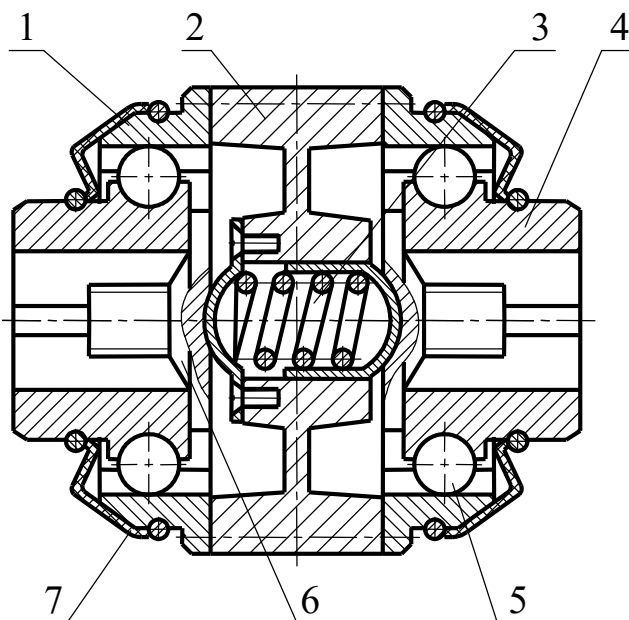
Кулькова компенсуюча муфта: 1 - обойма; 2 - проміжний диск; 3 - пружинний амортизатор; 4 - півмуфта; 5 - кульки; 6 - болт; 7 - манжет
